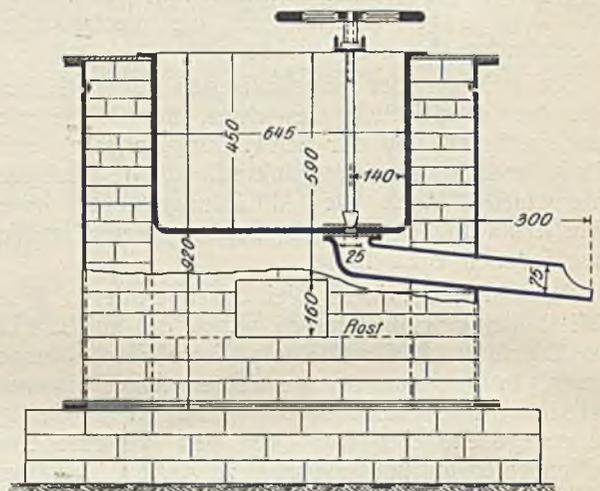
Gießanlage der Chemisch-Technischen Reichsanstalt. Maßstab 1 : 20.
